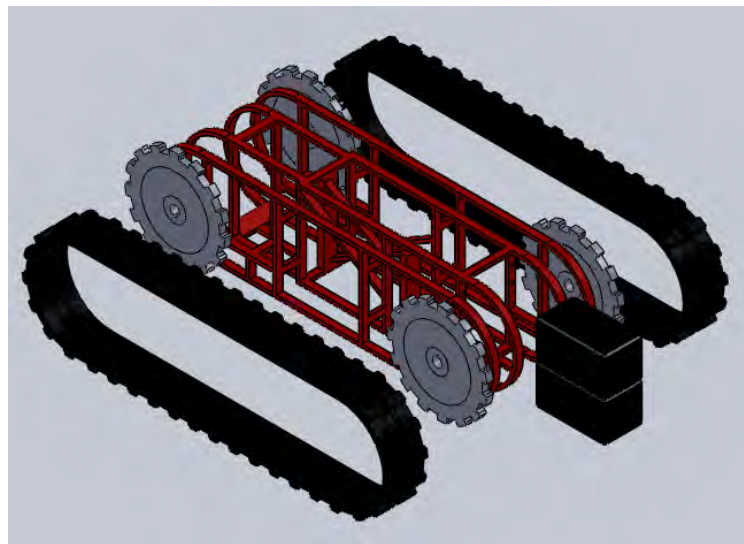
Vista explosionada de la primera fase del ensamblaje.
